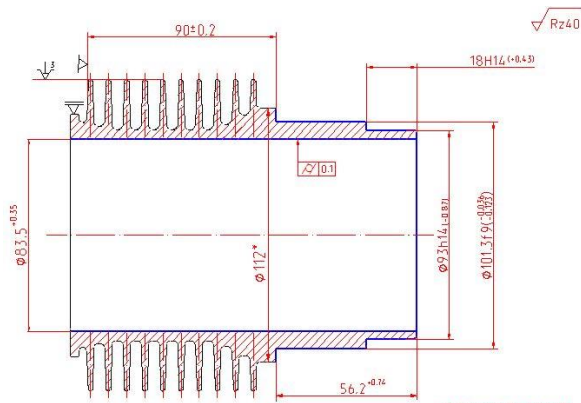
Эскиз обработки заготовки на токарном станке с ЧПУ
